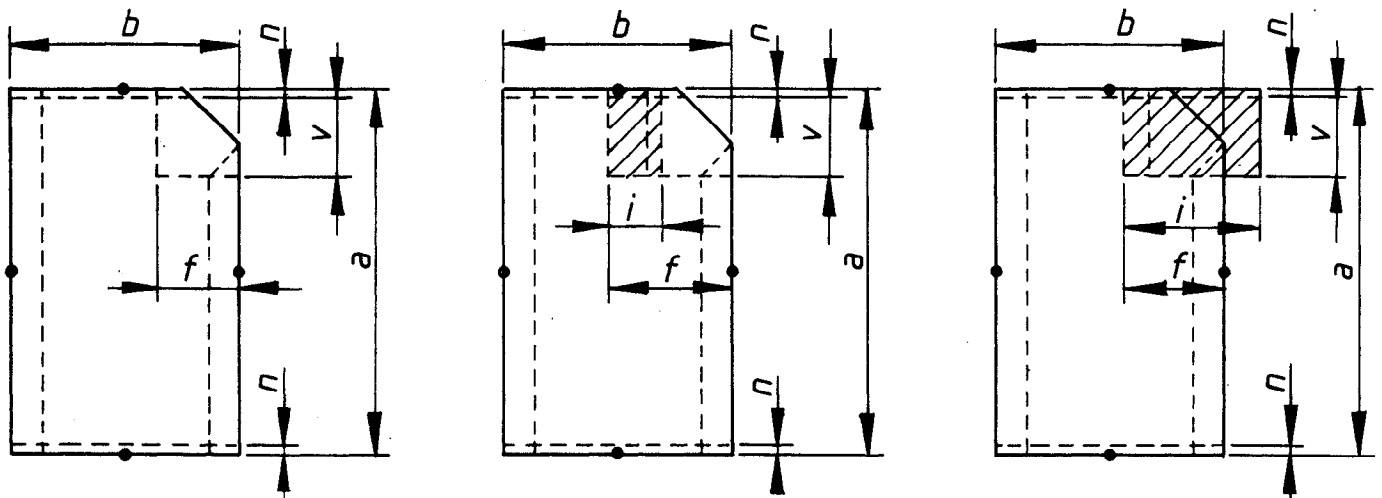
Sac à valve, soudé, à soufflets
